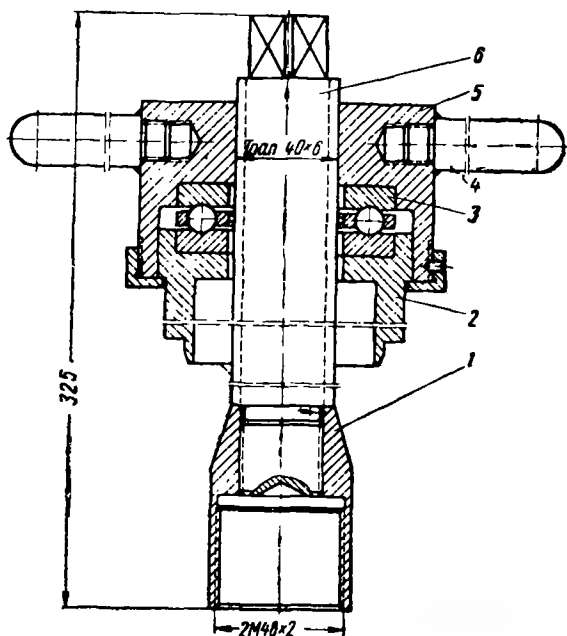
Приспособление для напрессовки якоря генератора управления ДК-405 на вал якоря ДК-403Г
